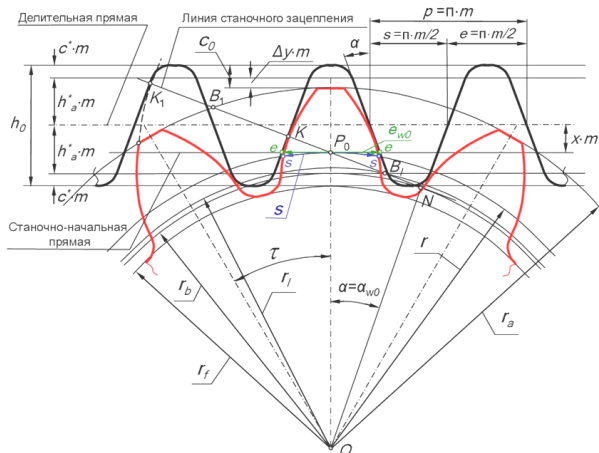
Верстатне зачеплення заготовки та модульної рейки
